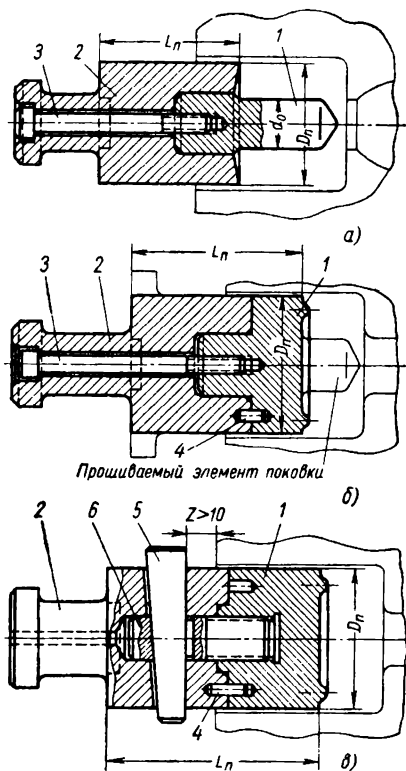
Сборный формовочный пуансон: а —  $D_n < 80$  мм; б —  $D_n = 80 \div 160$  мм; а —  $D_n > 160$  мм; 1 — пуансон; 2 — державка; 3 — винт; 4 — штифт; 5 — клин; 6 — штырь
